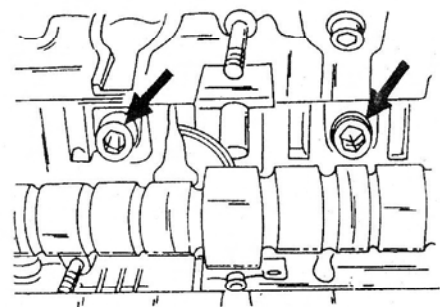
Стрелками указаны болты крепления опор подшипников рычагов коромысел.
